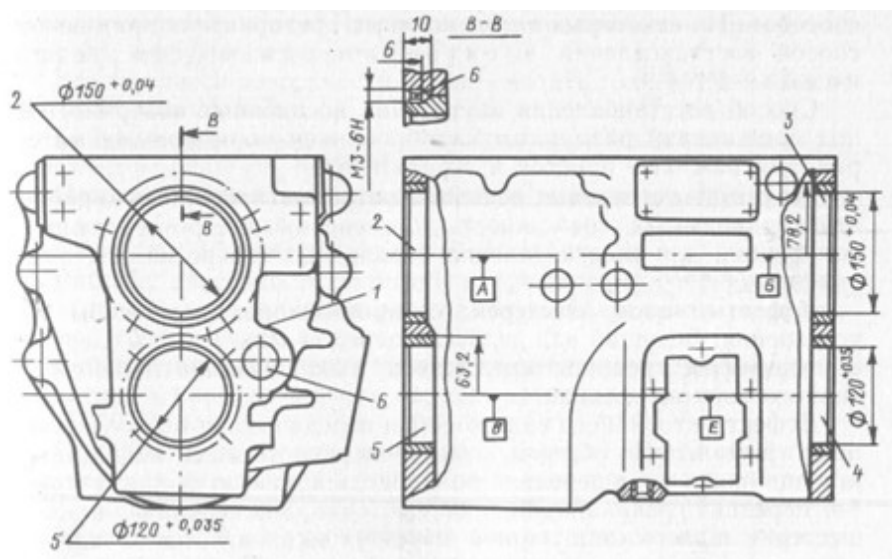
Места расположения возможных дефектов на картере коробки передач: 1 — трещины на стенке картера; 2, 3, 4, 5 — износ отверстий под подшипники первичного, вторичного и промежуточного валов коробки передач; 6 — износ отверстия под ось блока шестерен
